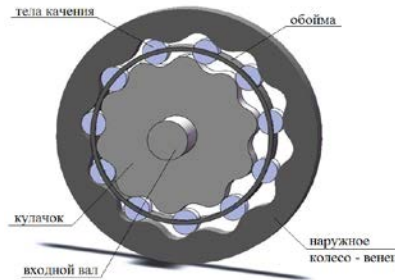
Схема зацепления передачи с промежуточными телами качения и свободной обоймой
